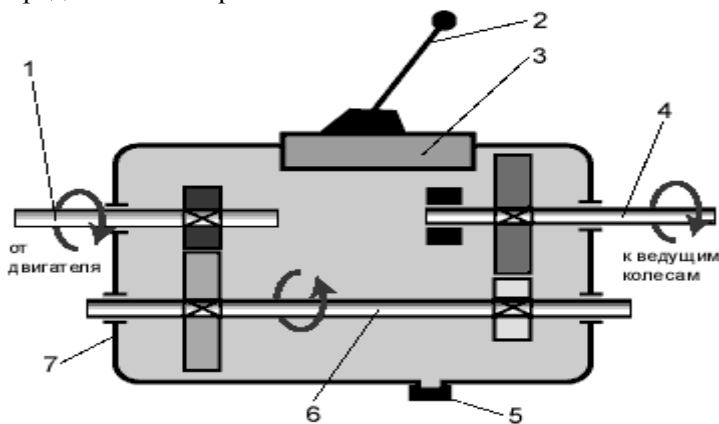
Схема работы коробки передач. 1 - первичный вал; 2 - рычаг переключения передач; 3 - механизм переключения передач; 4 - вторичный вал; 5 - сливная пробка; 6 - промежуточный вал; 7 - картер коробки передач
